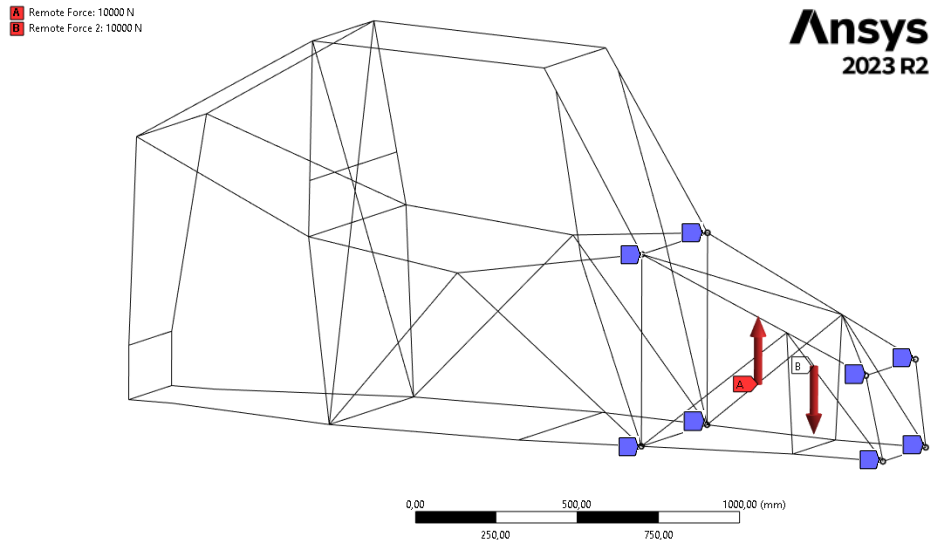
Preparación en ANSYS: Disposición del par de fuerzas del ensayo a torsión
